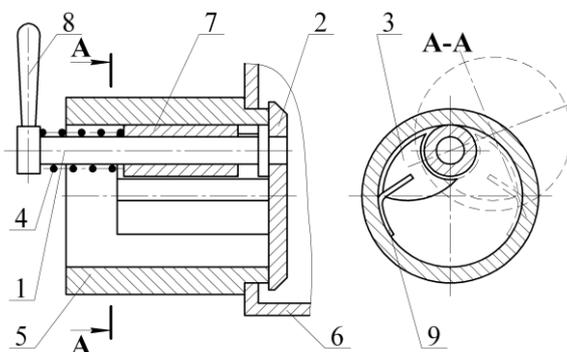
Ексцентриковий затвор: 1 – вал; 2 – запірний диск; 3 – лопать; 4 – пружина; 5 – порожниста опора; 6 – горловина бункера; 7 – втулка; 8 – ручка; 9 – еластичний елемент;
